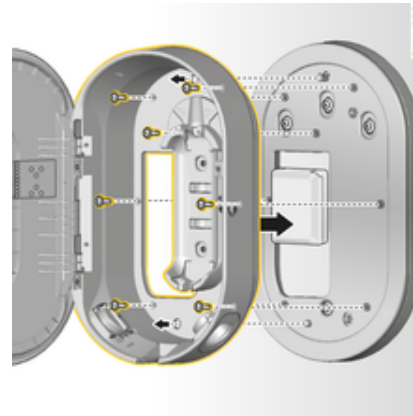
Atornillado del puerto de carga en la placa de montaje
